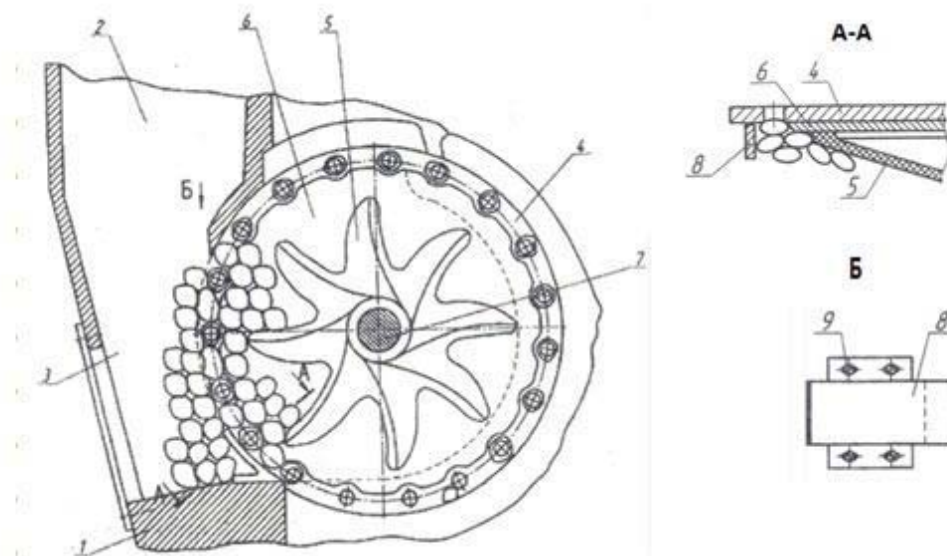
Схема частини пневмомеханічного висівного апарата
